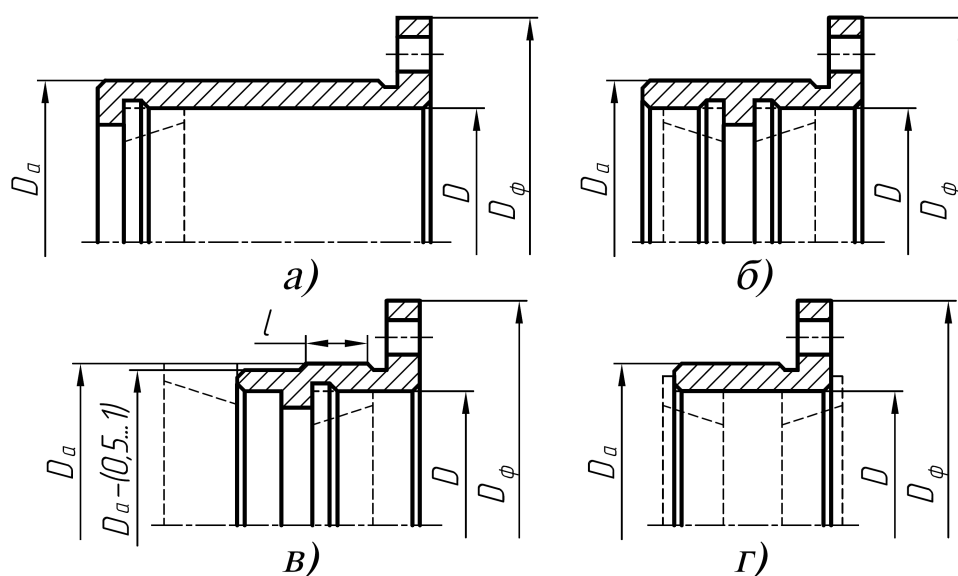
Приклади конструкцій стаканів для установки підшипників кочення (D – діаметр, спряжений з підшипниками кочення; D_a – діаметр зовнішньої циліндричної поверхні; D_ϕ – діаметр зовнішньої циліндричної поверхні фланця)
